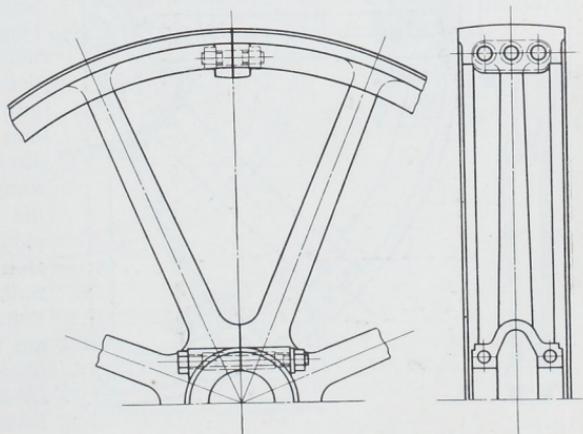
Zwischen den Armen geteiltes, an der Fuge bearbeitetes Rad.
